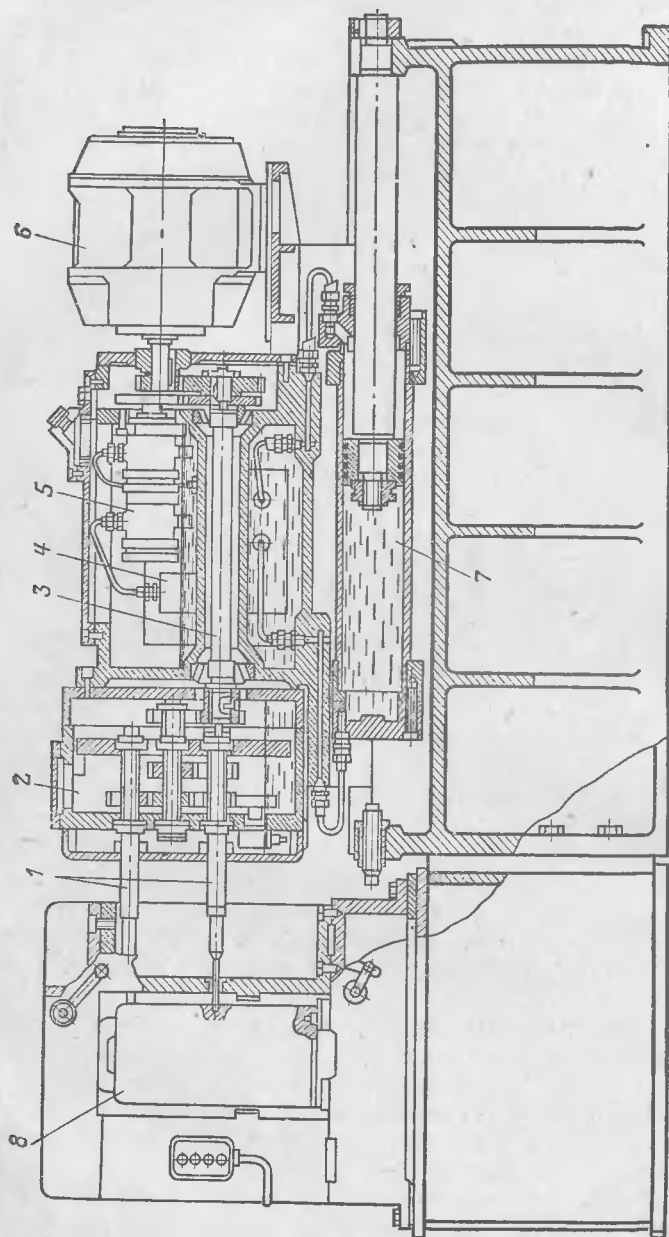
Самодействующая силовая головка агрегатного станка.
